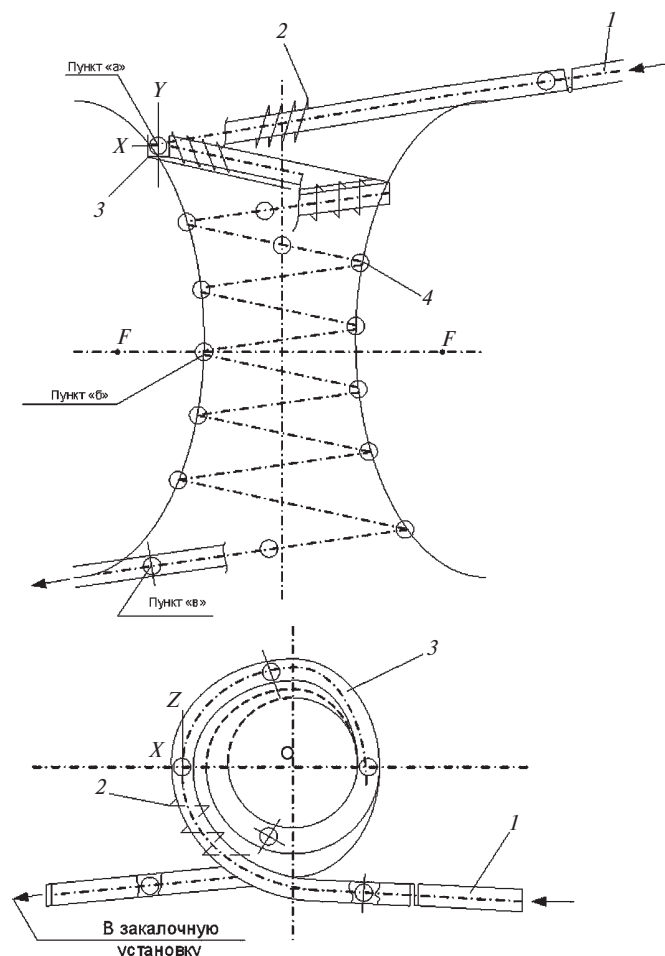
Установка непрерывного действия для индукционного нагрева изделий шарообразной формы с гиперболической образующей
